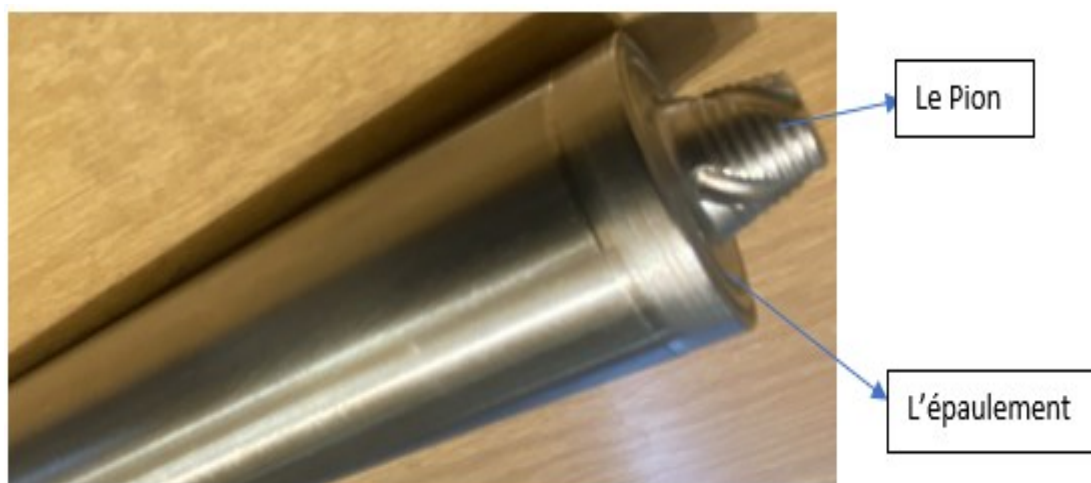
Outil à simple épaulement ou conventionnel utilisé pour le soudage
